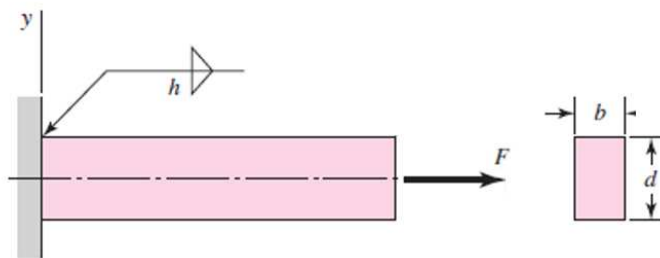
Voldadizo soldado sujeto a tensión.
